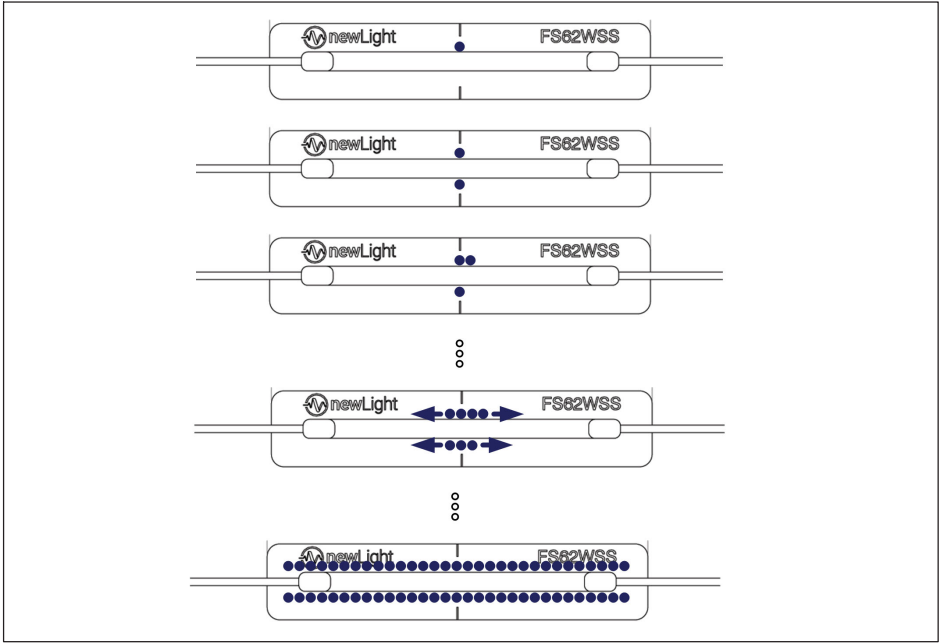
Schweißverfahren für FS62WSS BRD
